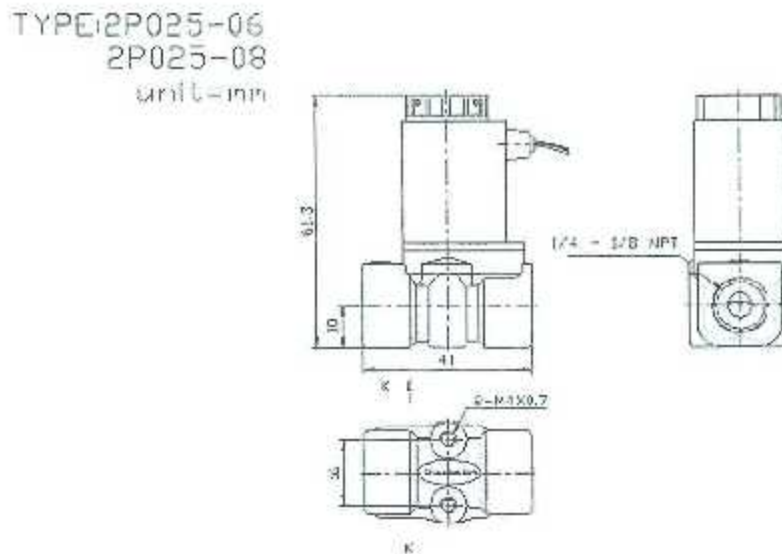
Dimensiones electroválvula 2P025-08 [5].
